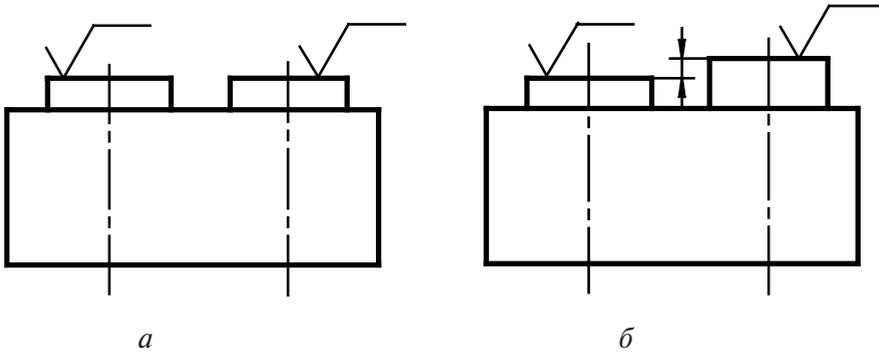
Конструкция корпусных деталей с бобышками:
